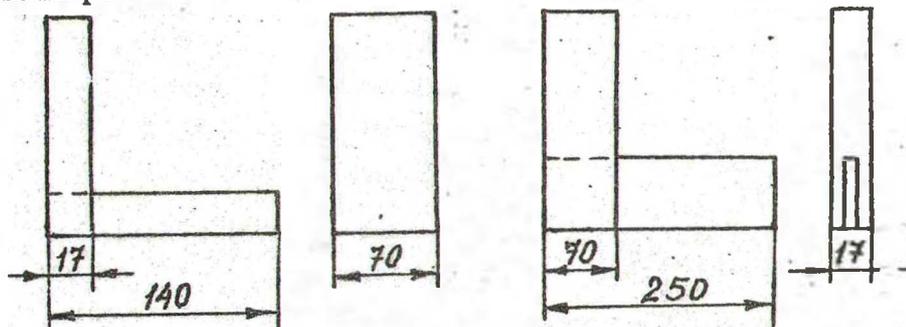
Схемы образцов и элементов шиповых соединений: а - угловое ящичное на шип прямой открытый; б - угловое концевое на шип открытый сквозной одинарный
